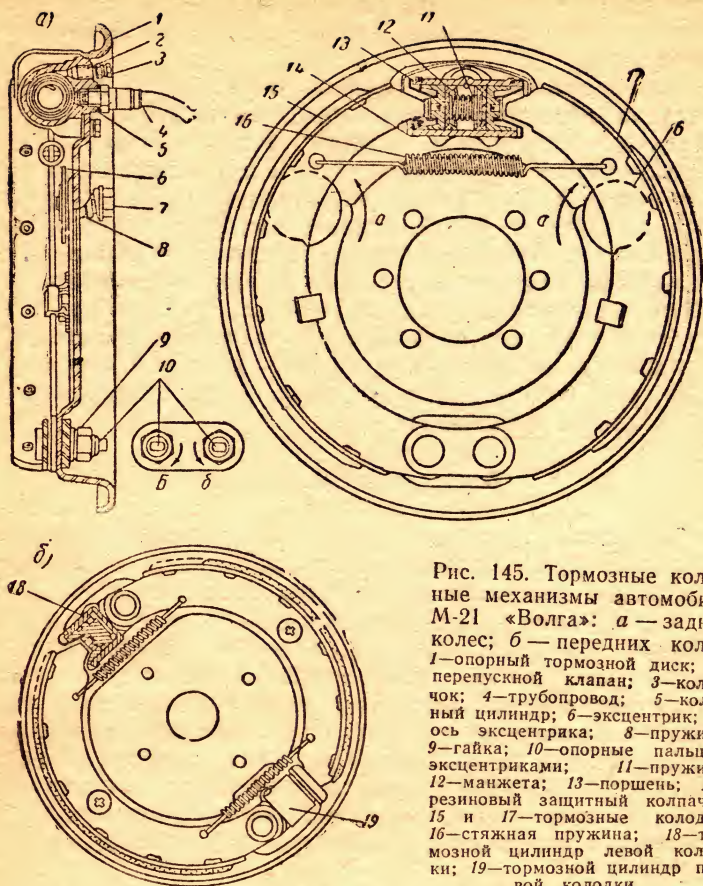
Тормозные колесные механизмы автомобиля М-21 «Волга»: а — задних колес; б — передних колес; 1—опорный тормозной диск; 2—перепускной клапан; 3—колпачок; 4—трубопровод; 5—колесный цилиндр; 6—эксцентрик; 7—ось эксцентрика; 8—пружина; 9—гайка; 10—опорные пальцы с эксцентриками; 11—пружина; 12—манжета; 13—поршень; 14—резиновый защитный колпачок; 15 и 17—тормозные колодки; 16—стяжная пружина; 18—тормозной цилиндр левой колодки; 19—тормозной цилиндр правой колодки
